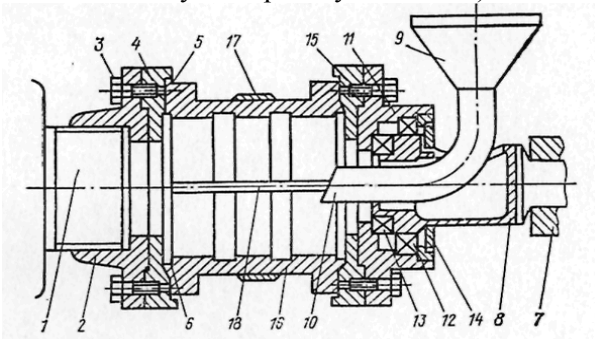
Пристосування для відцентрового заливання вкладишів підшипників ковзання: 1 – шпindel токарного верстата; 2 – передня; 3 – болти; 4 – передній натискний диск; 5, 6 – виїмки в диску; 7 – задня бабка токарного верстата; 8 – шпindel пристосування; 9 – воронка; 10 – носик воронки; 11 – задня планшайба пристосування; 12, 13 – шарикопідшипники; 14 – затискна тарілка; 15 – задній знімний диск; 16 – вкладиш; 17 – хомут для стяжки вкладиша; 18 – прокладки
